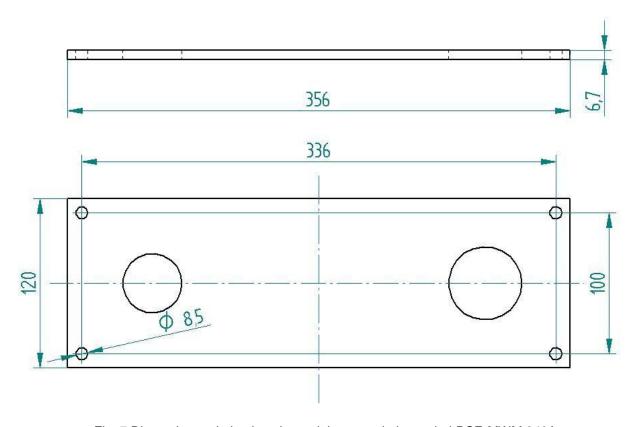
Dimensiones de la placa base del sensor de humedad PCE-MWM 240A
